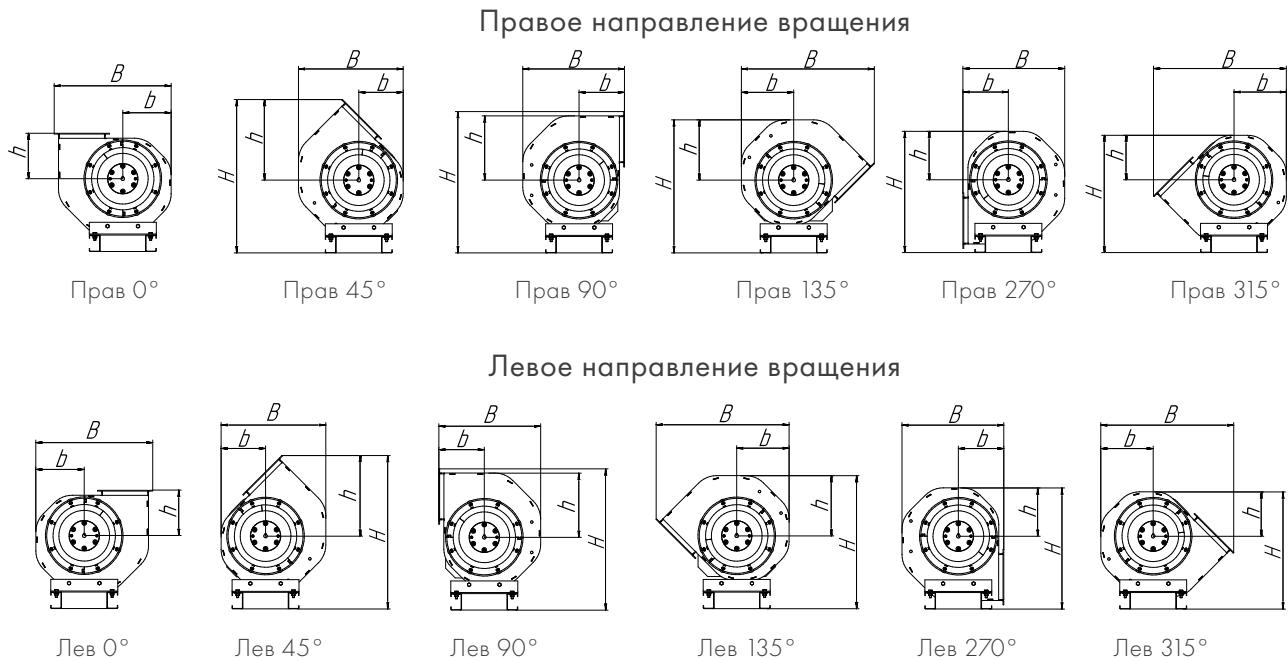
Направление вращения и углы разворота спирального корпуса
